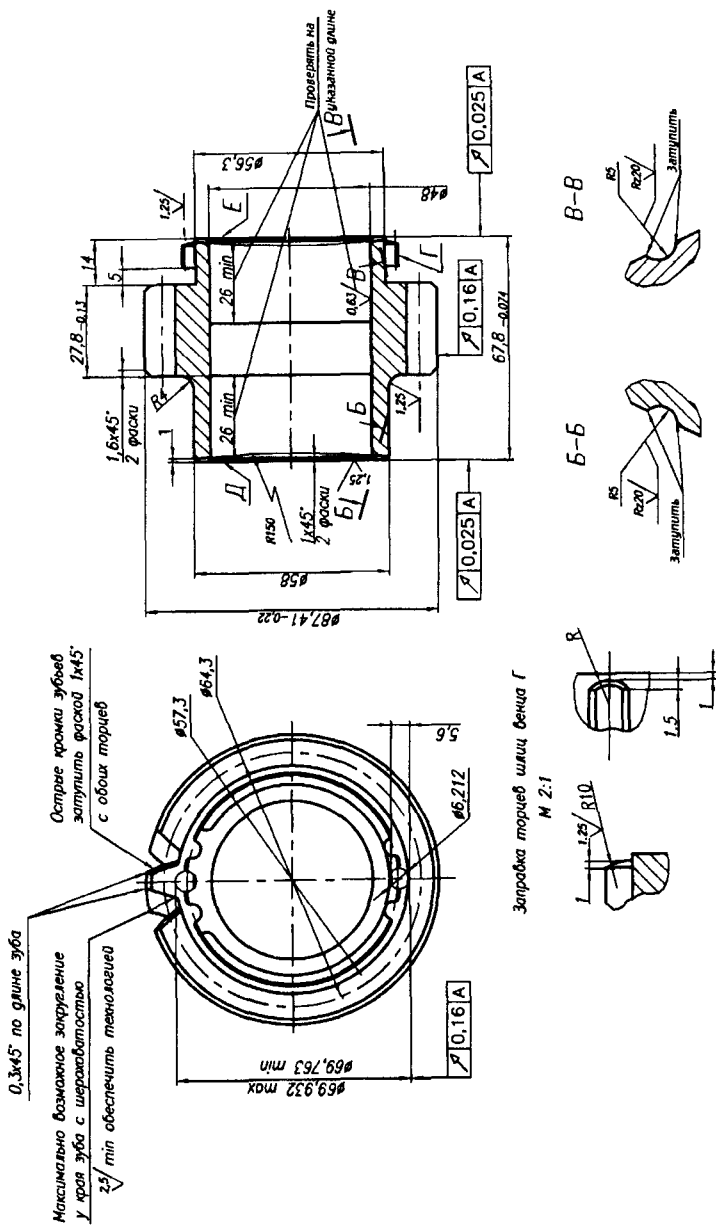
Шестерня вала коробки отбора мощности автомобиля
